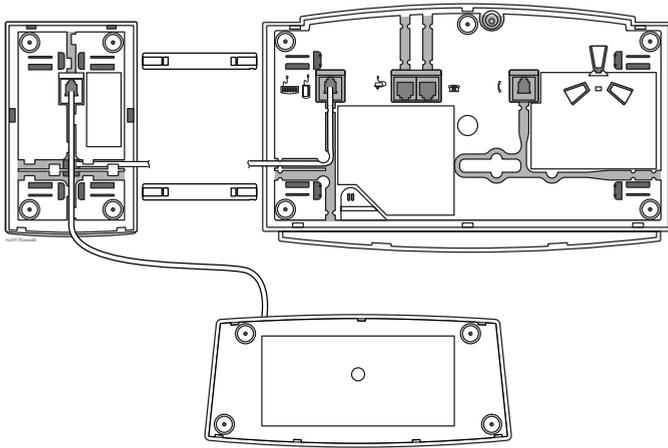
Montaggio dell'AKB sull'esempio dell'Office 45 con EKP
